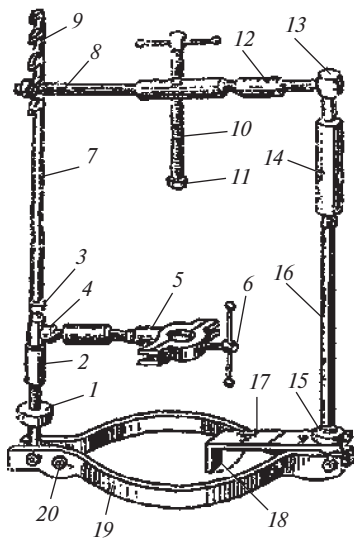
Приспособление для ремонта задвижек под высоким давлением газа:
